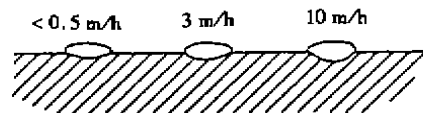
堆焊速度对堆焊焊缝成形的影响
